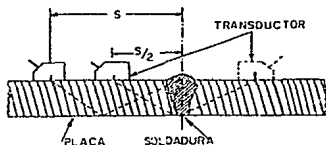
Inspección con haz angular de una unión soldada a tope.
